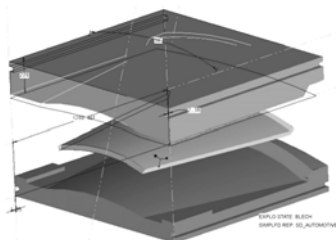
Схема прессования заготовки в сегмент. Заготовка расположена внутри формообразующих стальных вставок штампа [26]
